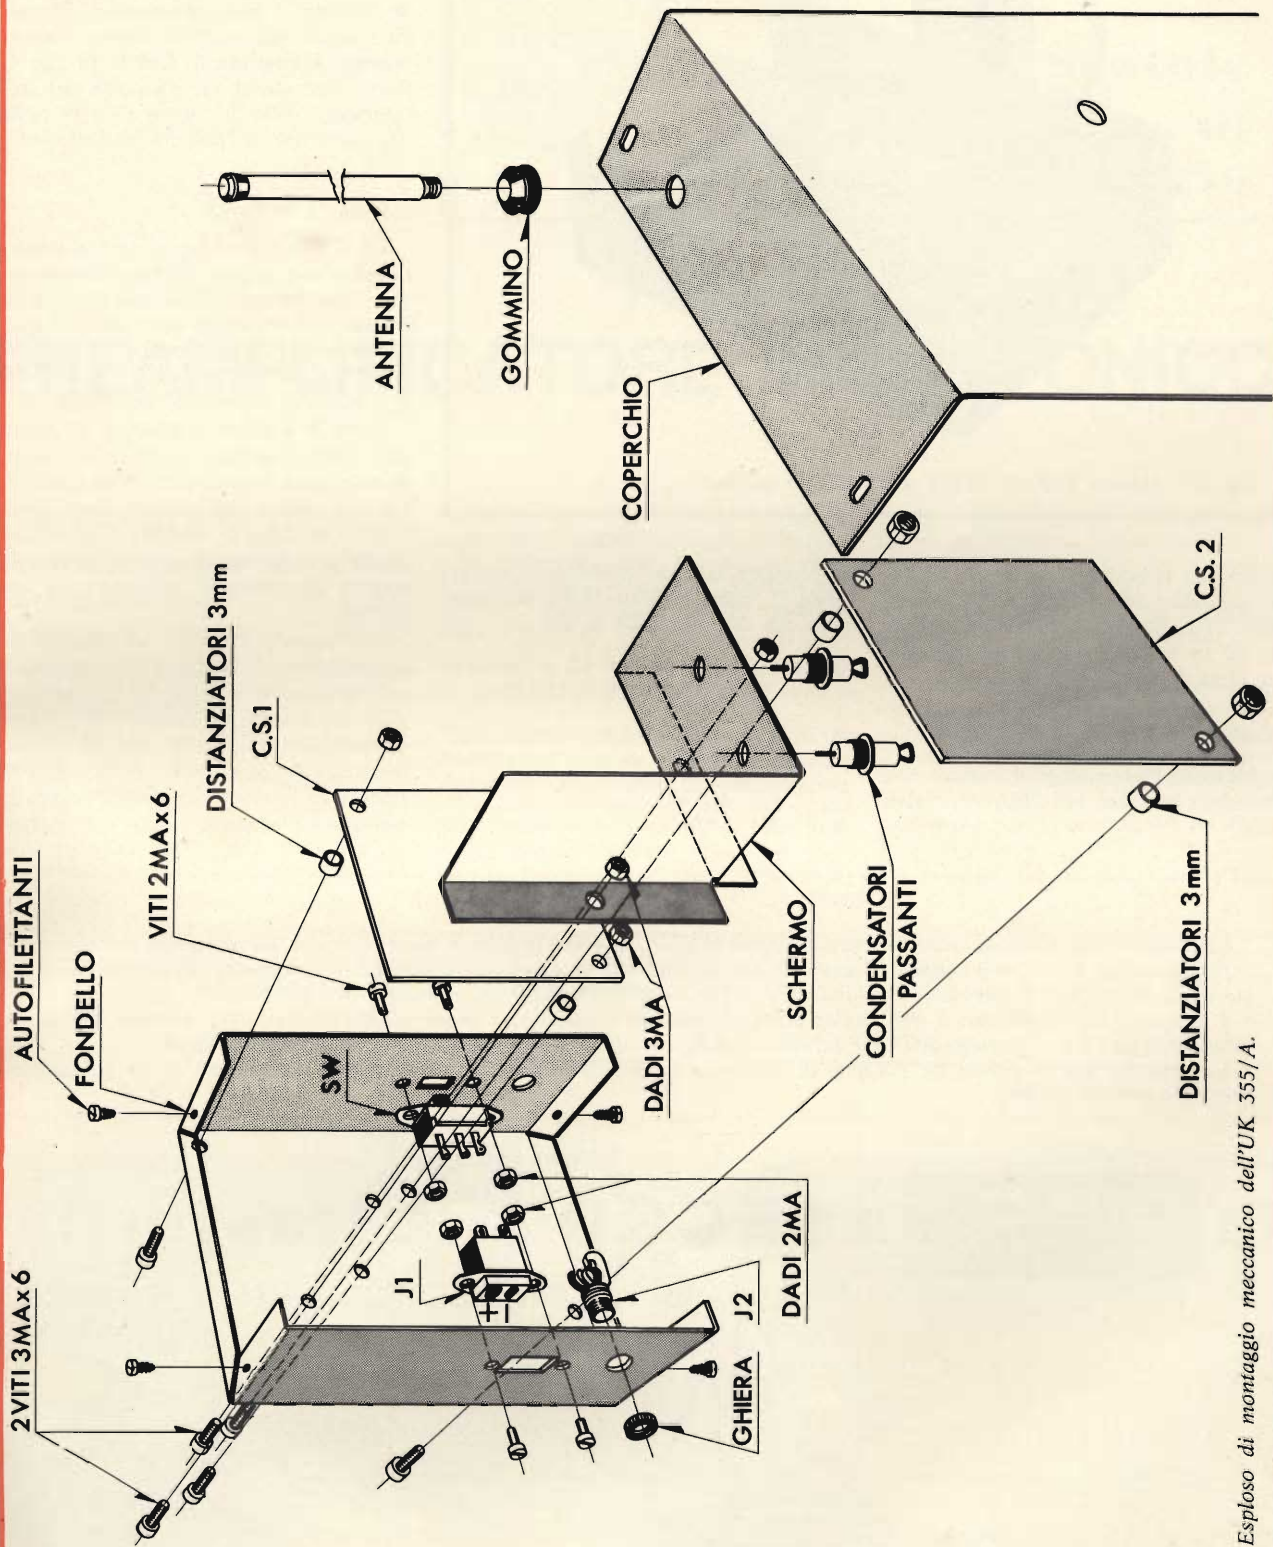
Esploso di montaggio meccanico dell'UK 555/A.
